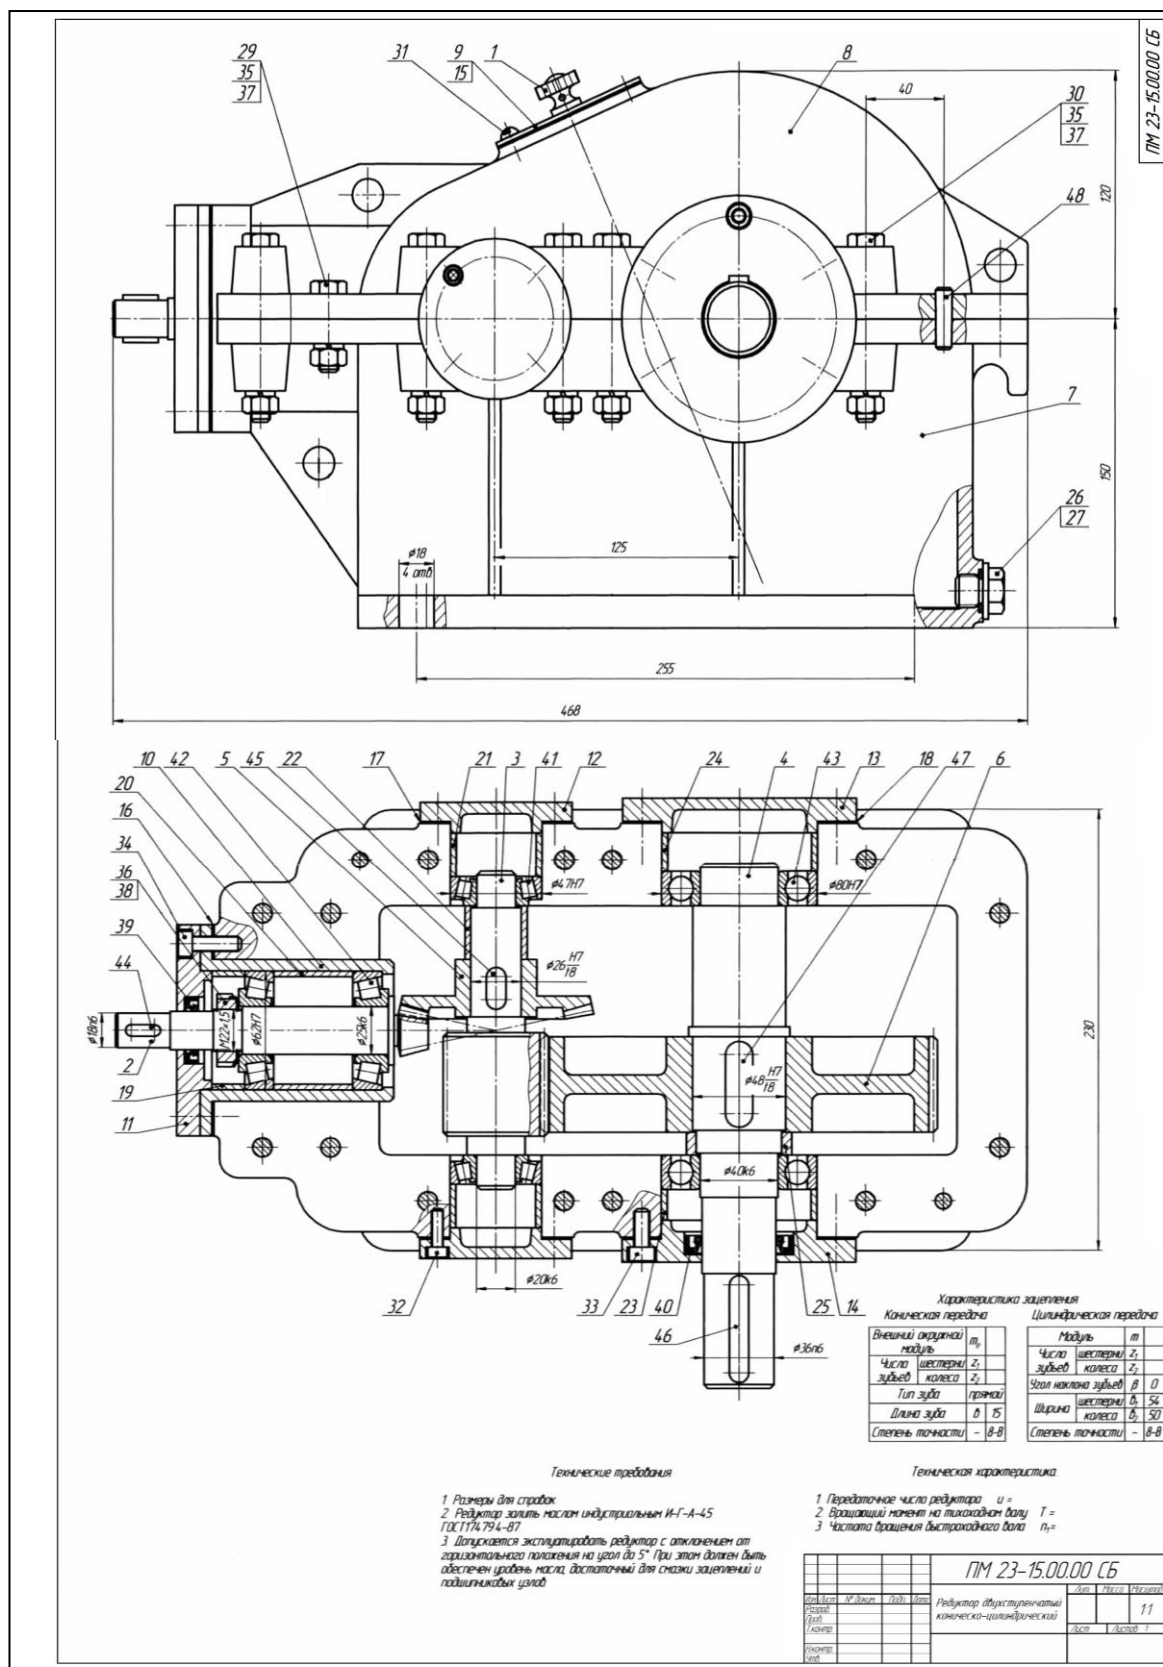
Пример сборочного чертежа двухступенчатого коническо-цилиндрического редуктора
